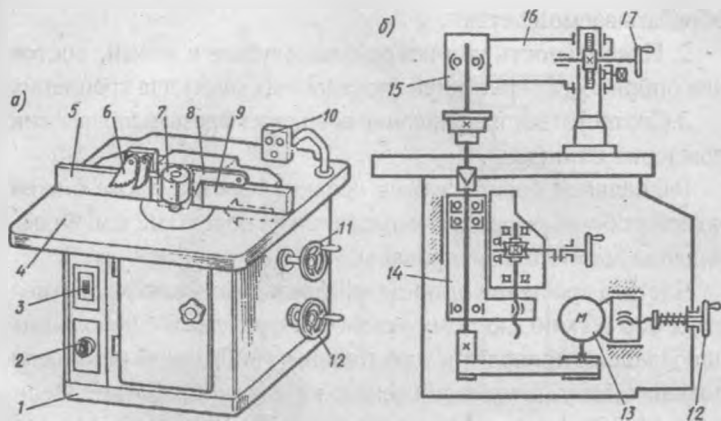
Одношпиндельный фрезерный станок с ручной подачей ФС-1:
